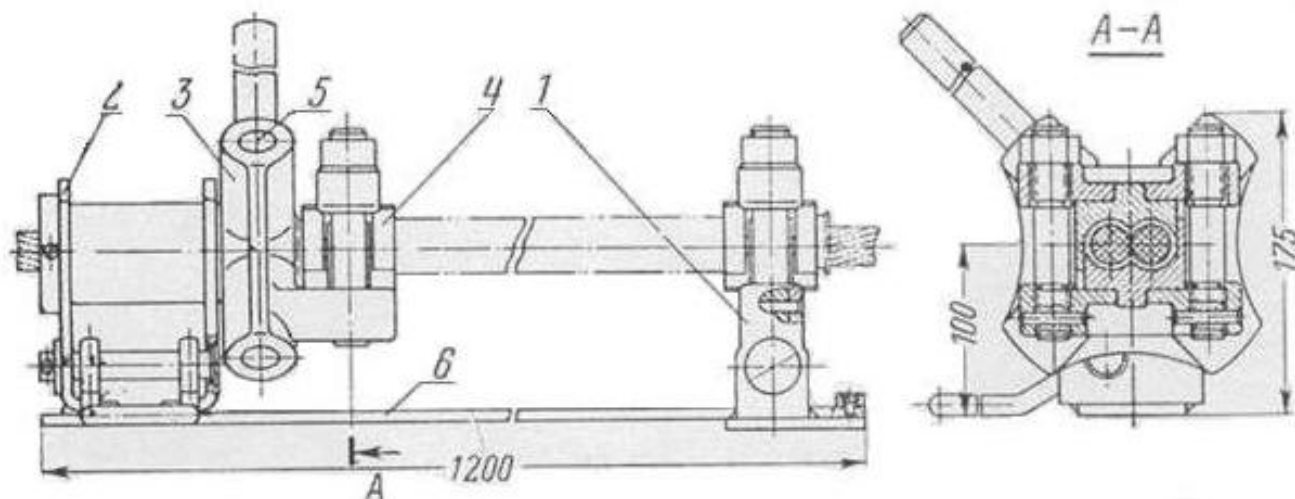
Приспособление МИ-230А для скручивания овальных соединителей:
